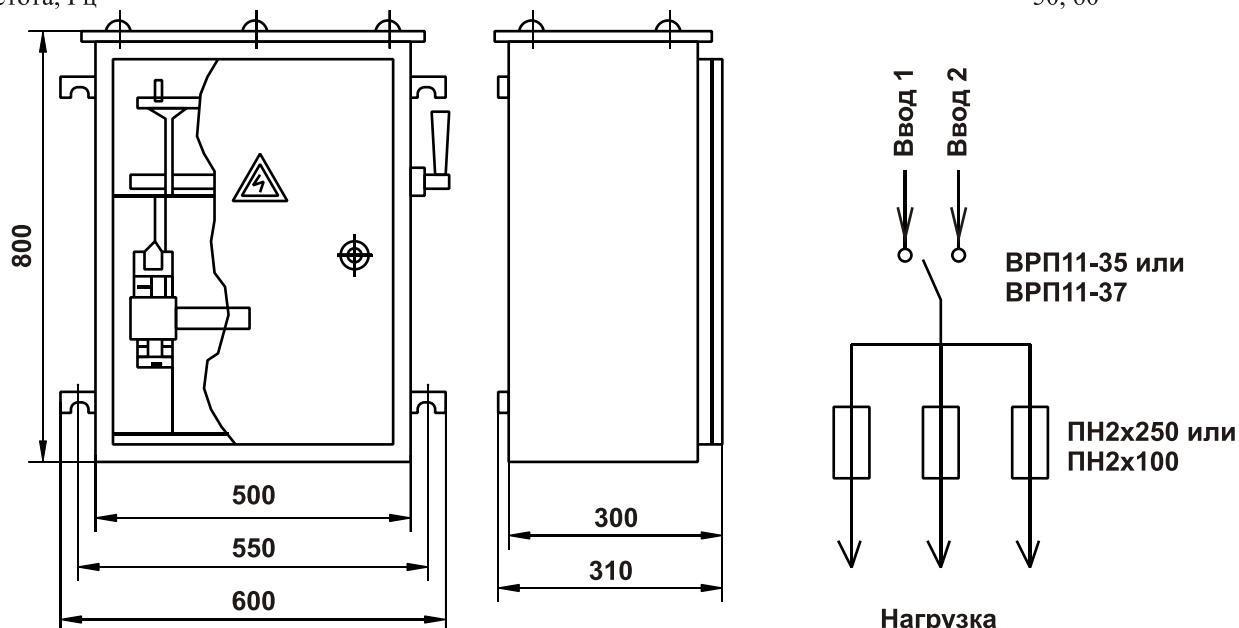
Внешний вид и габаритные размеры ЯВП
